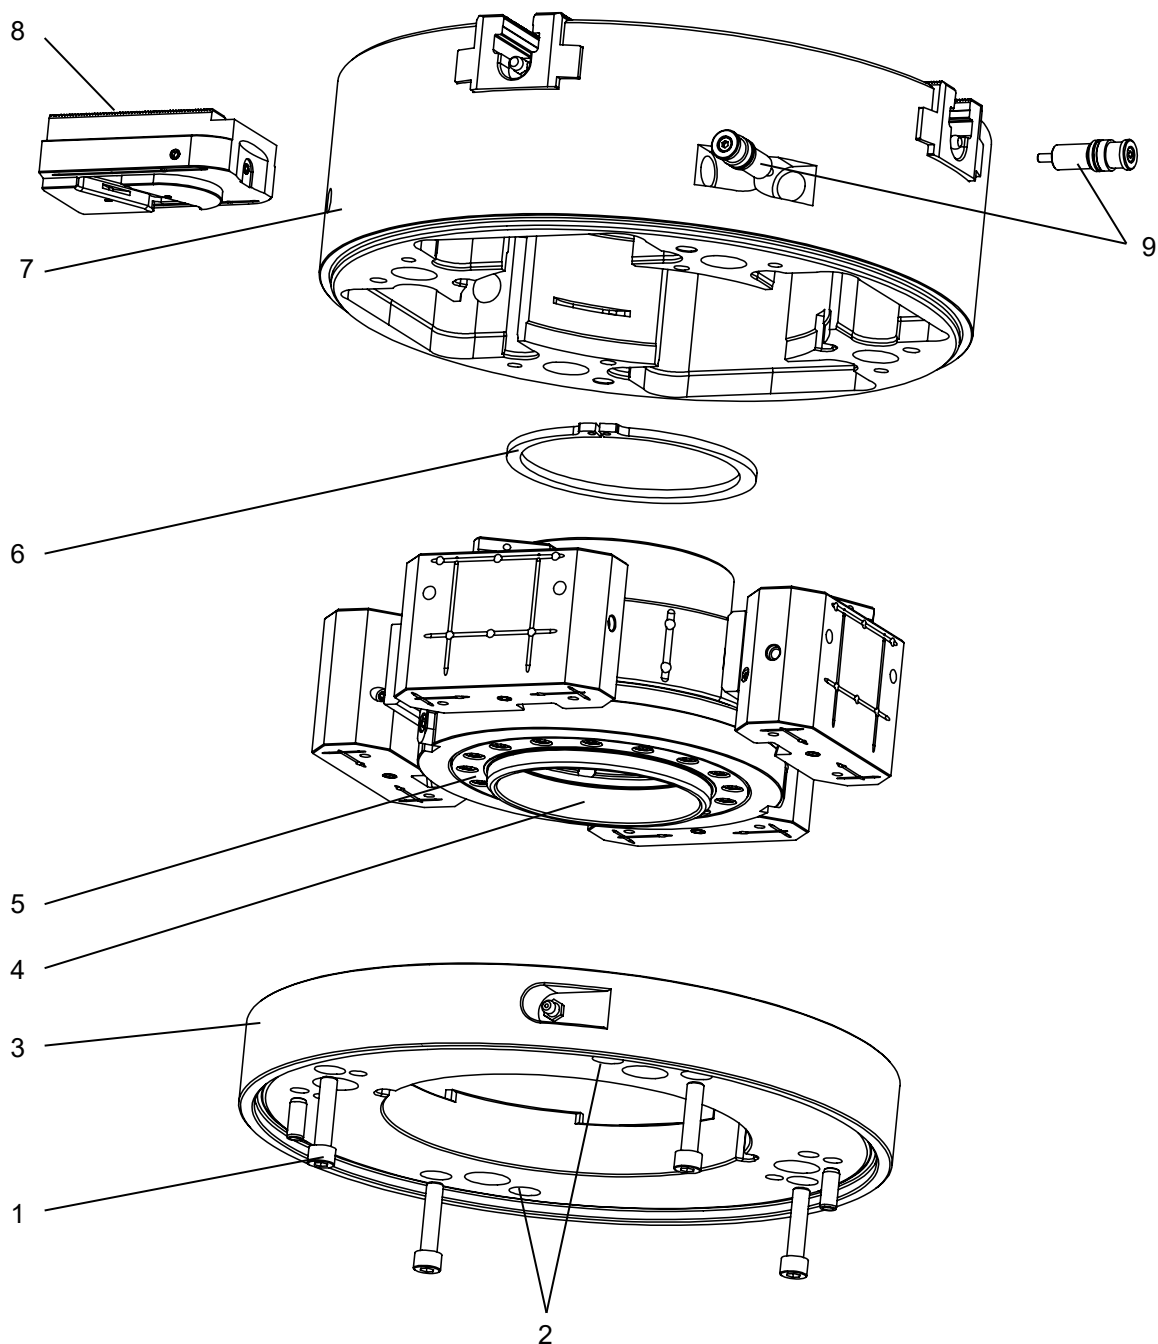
Smontaggio/montaggio del mandrino di serraggio (VT-S 013 – VT-S 080)
